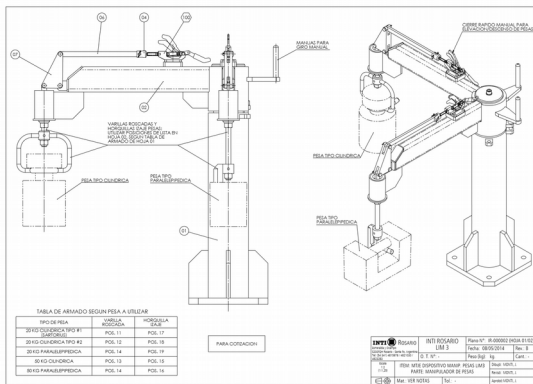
Plano Cjto. Dispositivo Manipulador de Pesas.
